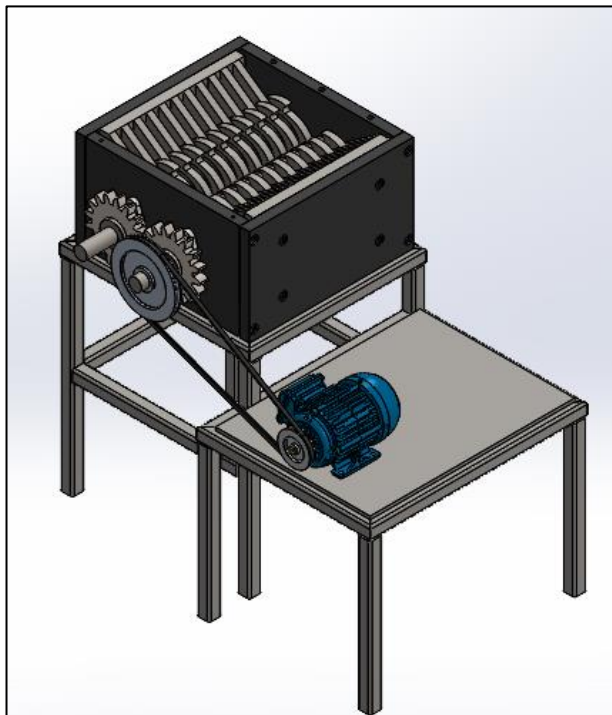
Vista isométrica del ensamblaje final de la máquina trituradora en SolidWorks
